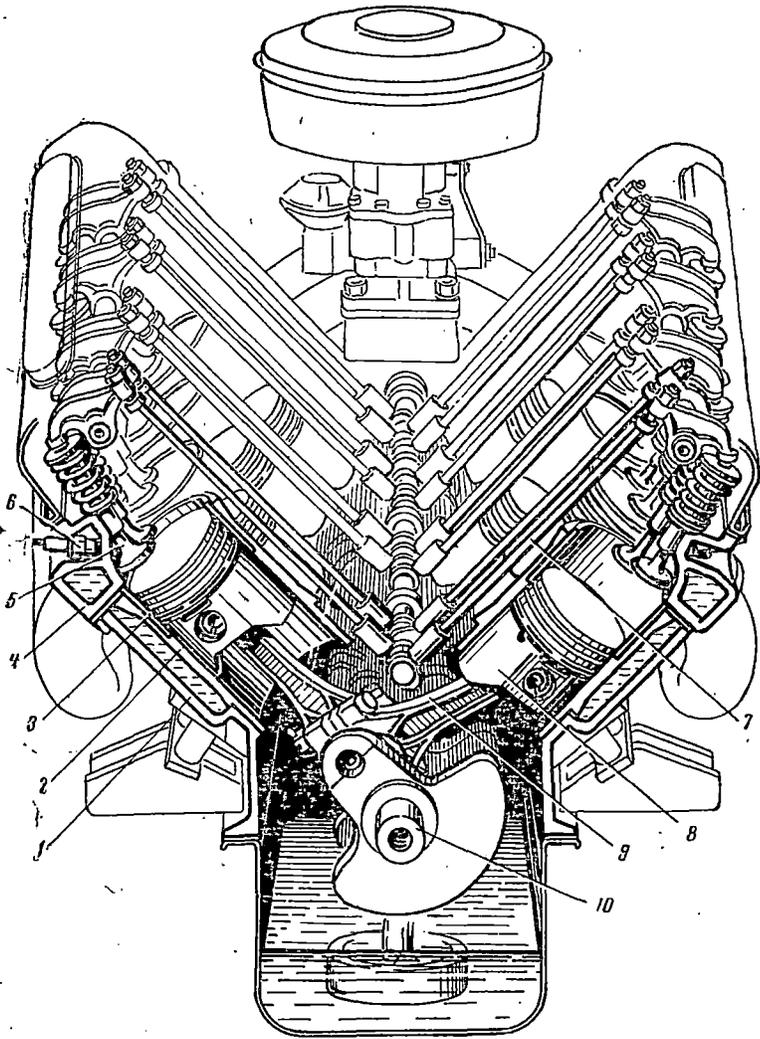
Схематический разрез двигателя ЗМЗ-53:
